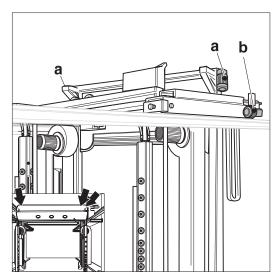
Motores reductores a Motor elevador – barra de techo de alta presión
